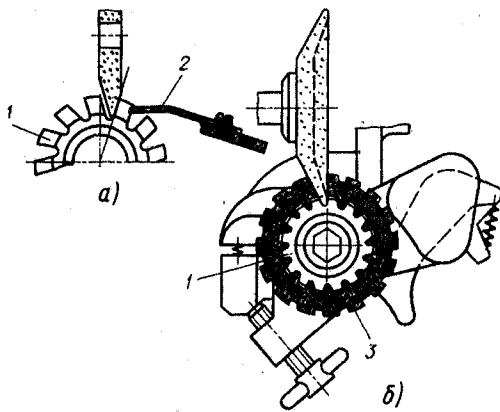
Схемы фиксации фрезы при заточке по передней поверхности с помощью упорки (а) или делительного приспособления (б)
